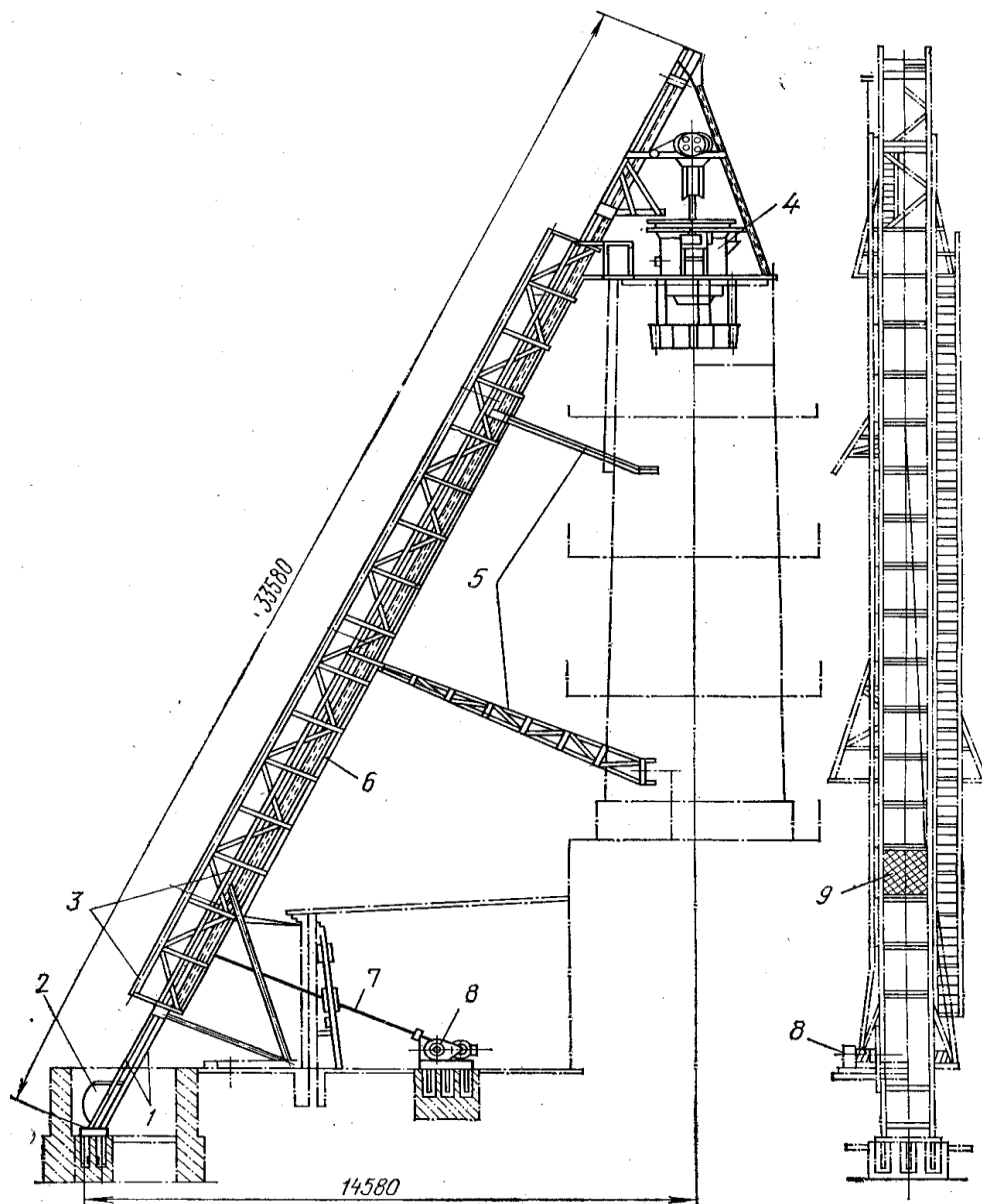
Схема скипового загрузочного устройства шахтных печей:
